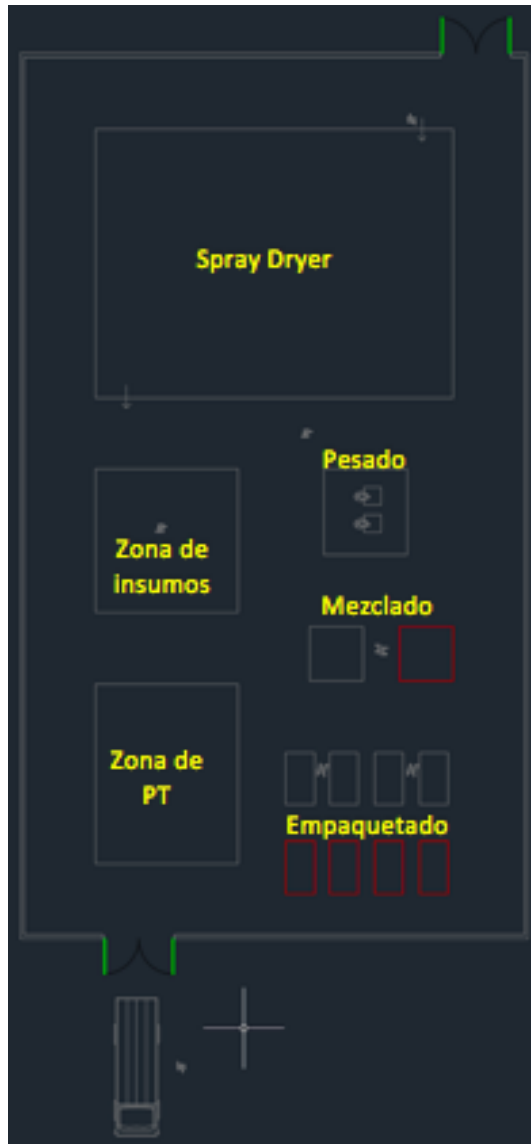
Layout de la nueva sección de jugo en polvo con las máquinas actuales y las futuras.
